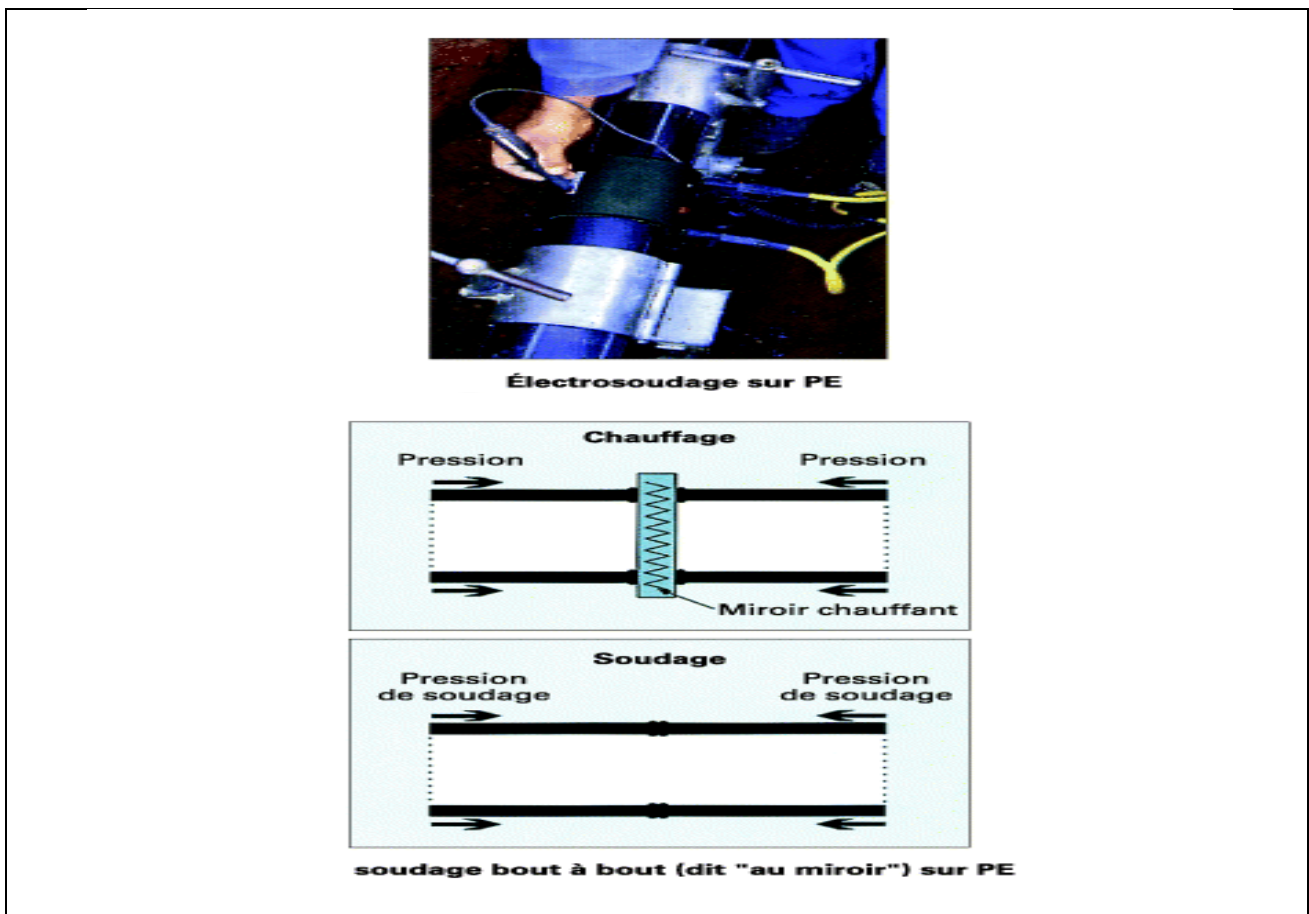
Electrosoudage et soudage bout à bout.
